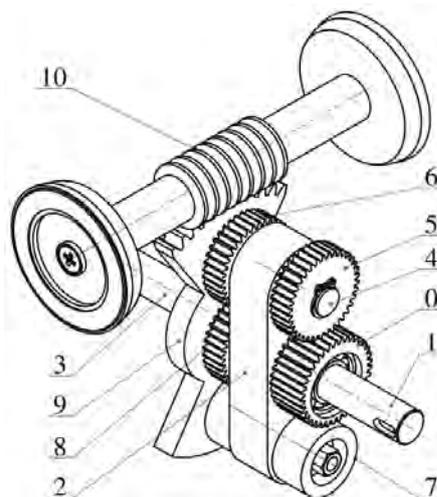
Конструкция предлагаемого планетарного зубчатого механизма компрессора: 0 – солнечное эллиптическое зубчатое колесо (неподвижно); 1 – входной вал; 2 – водило; 3 – выходной вал; 4 – вал сателлита; 5, 6 – эллиптические шестерни сателлита; 7 – противовес; 8 – эллиптическое колесо; 9 – зубчатый сектор; 10 – зубчатая рейка с поршнями
